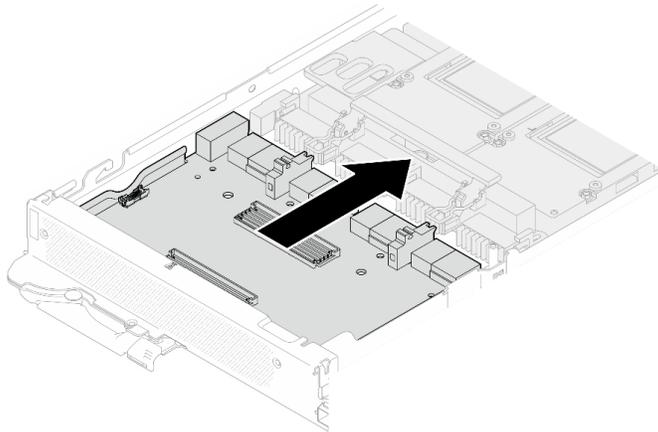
Conexión de la placa del transportador a la placa de la GPU.
